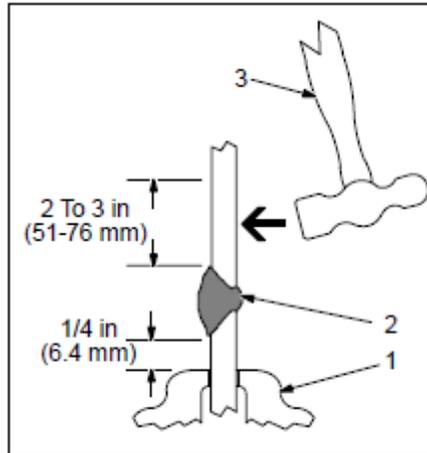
Prueba de resistividad de la soldadura
